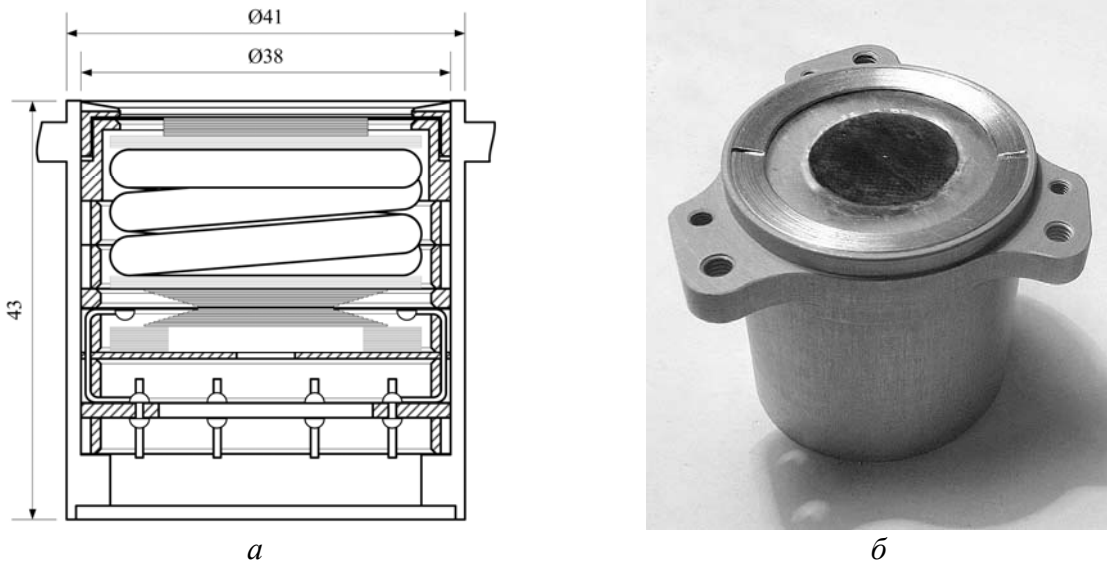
Сборочный чертеж (а) и внешний вид (б) блока датчиков
